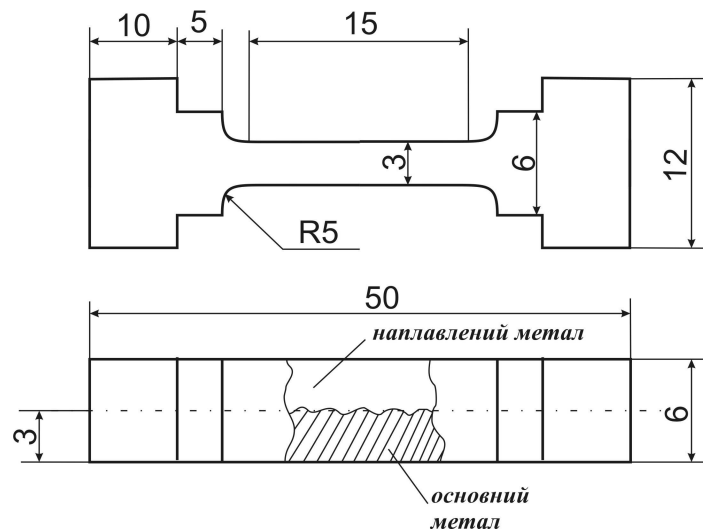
Геометрія зразка для випроб розтягом та схема його вирізання з двошарової заготовки з основного металу і наплавленого шару
